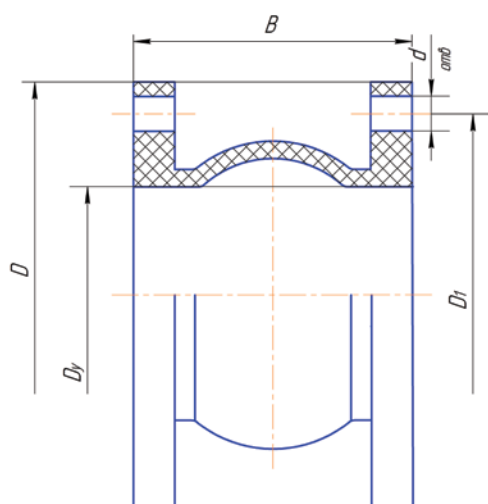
Габаритные и присоединительные размеры предлагаемых вставок.
